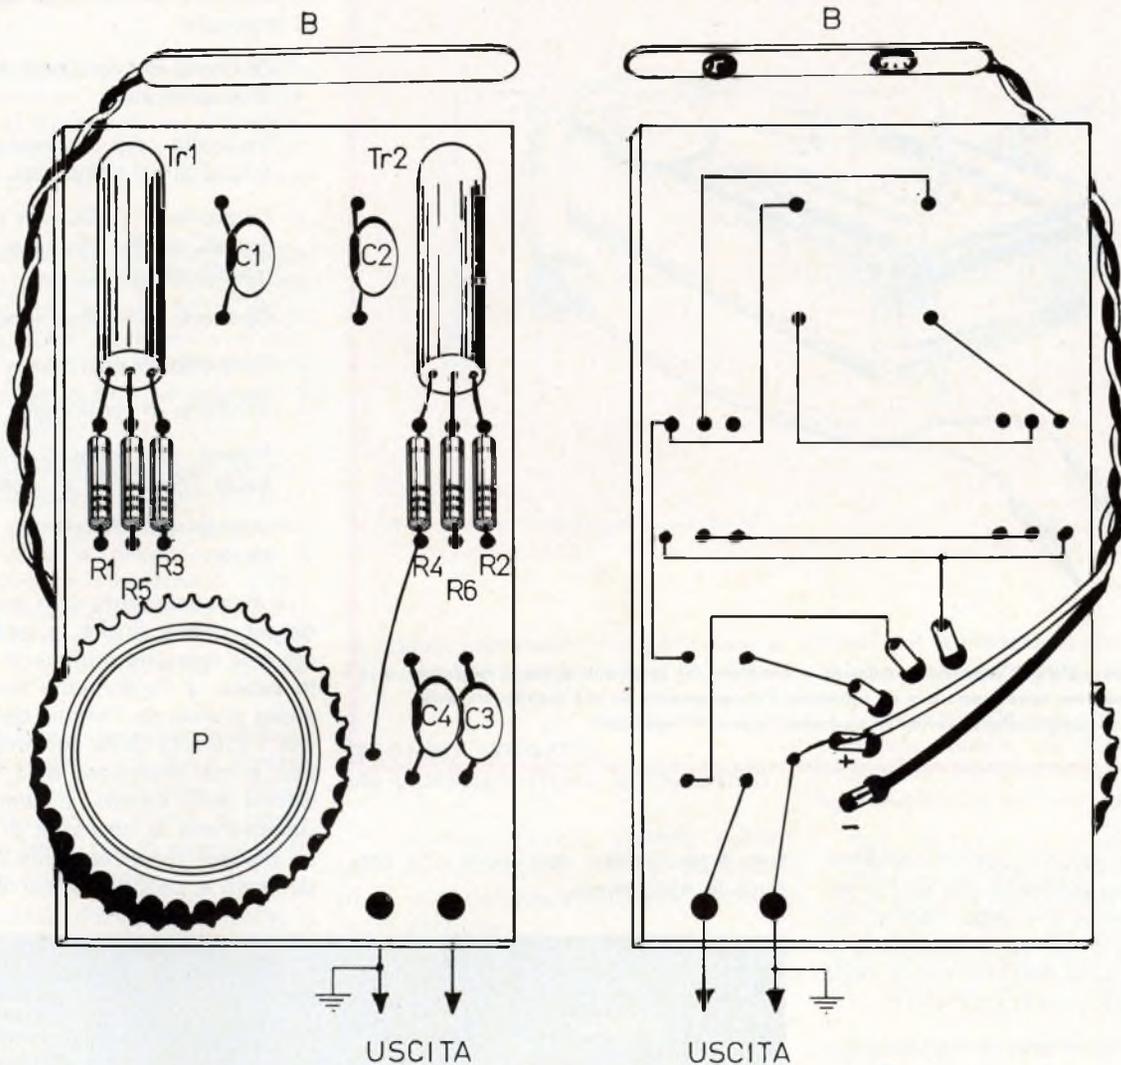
Aspetto del circuito montato, visto dal lato dei componenti a sinistra e delle connessioni a destra. Il cavetto schermato deve essere collegato ai due occhielli di maggiori dimensioni, facendo attenzione affinché la calza metallica sia in contatto col lato recante il simbolo di massa.
